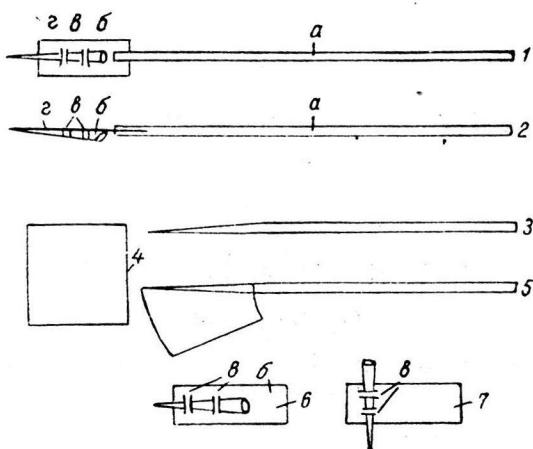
Детали и моменты изготовления пишущей части приспособления для чернильной записи.
